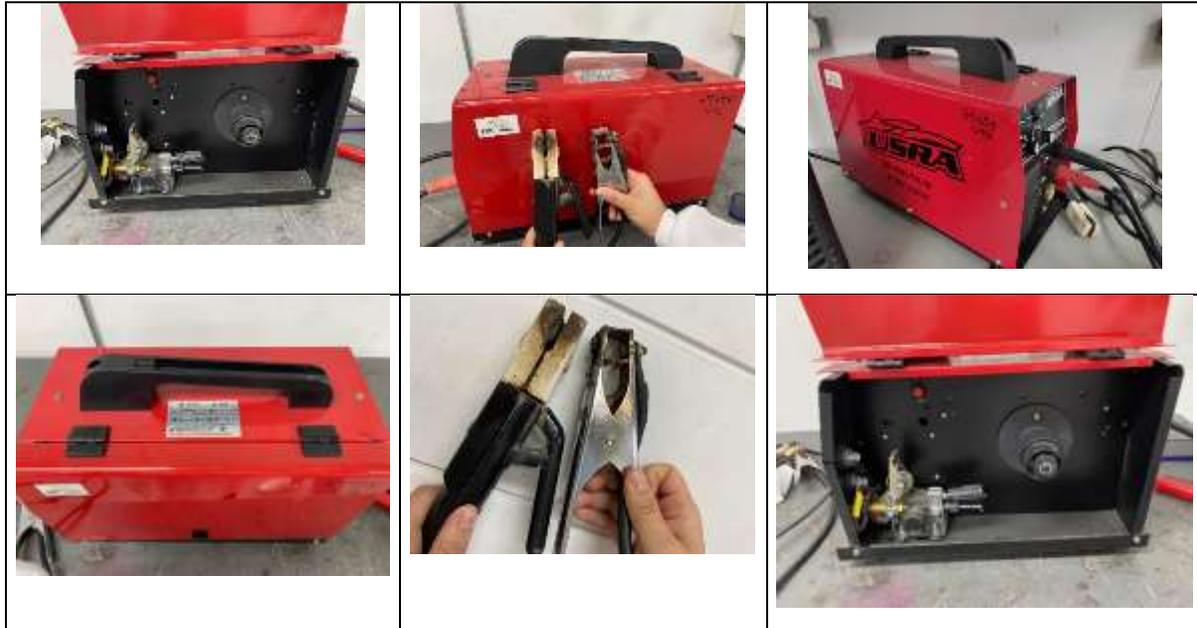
Equipo de corte con plasma antes de la rutina de mantenimiento preventivo
